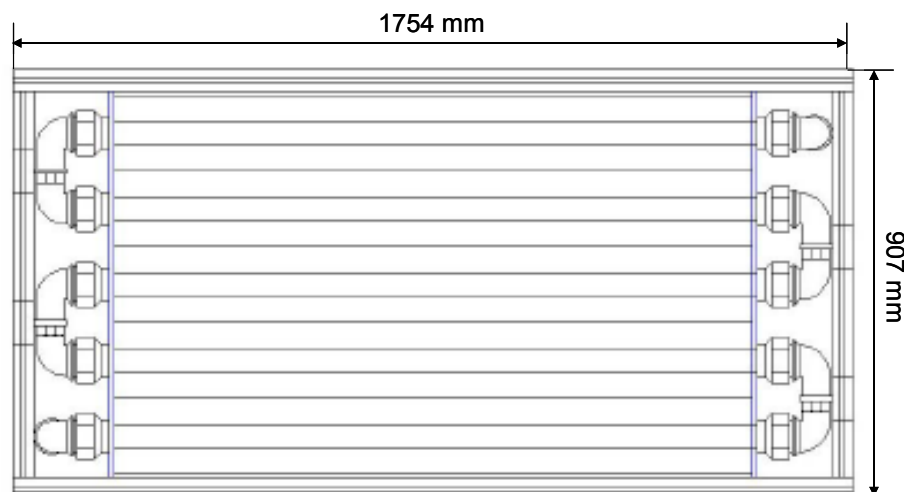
Vista superior del colector de configuración coaxial (dimensiones de colector de aletas: 1754 x 938 mm).
